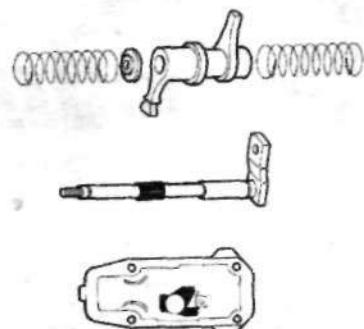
Снятие крышки вала включения передач на 5-ступенчатой коробке передач (раздел 8).
